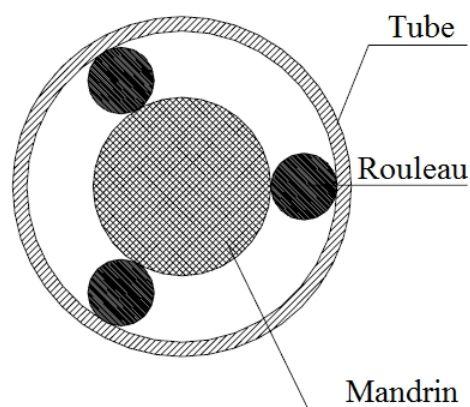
Coupe transversale d'un dispositif à trois rouleaux [4]
